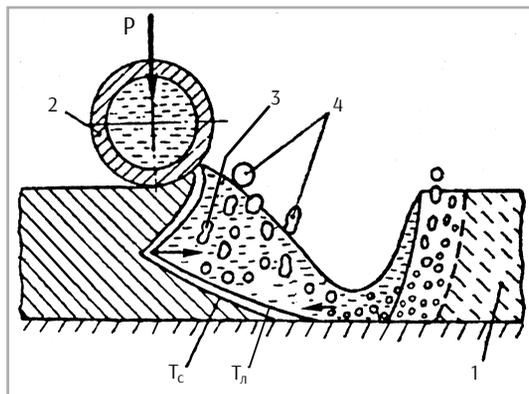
Схема высокотемпературной прокатки в процессе сварки: 1 — свариваемое изделие; 2 — ролик; 3 — сварочная ванна; 4 — пузырьки газа; P — давление ролика; T_C — зона солидуса; T_L — зона ликвидуса
